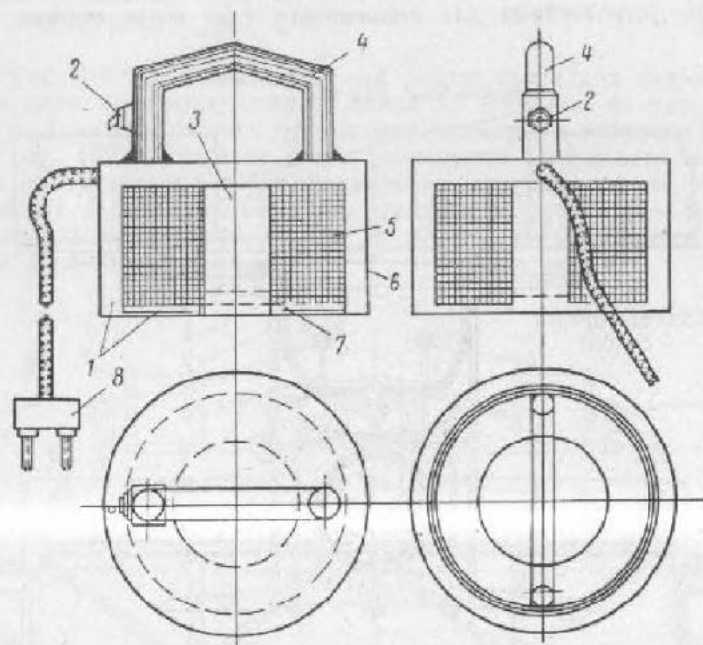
Электромагнитный сборочно-сварочный прижим.
